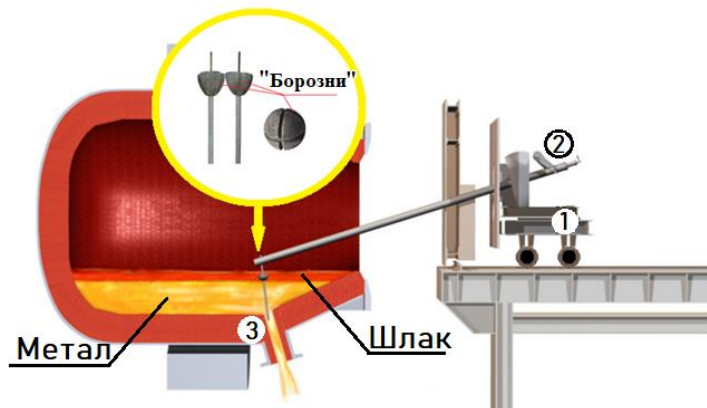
Загальний схематичний вигляд системи вторинного відсікання кінцевого конвертерного шлаку: 1 - аплікатор (маніпулятор) типу «візок» для подачі стопору в порожнину конвертера, 2 – механічний привід від'єднання стопору від штанги, 3 – сталевипускний канал (лютка).
